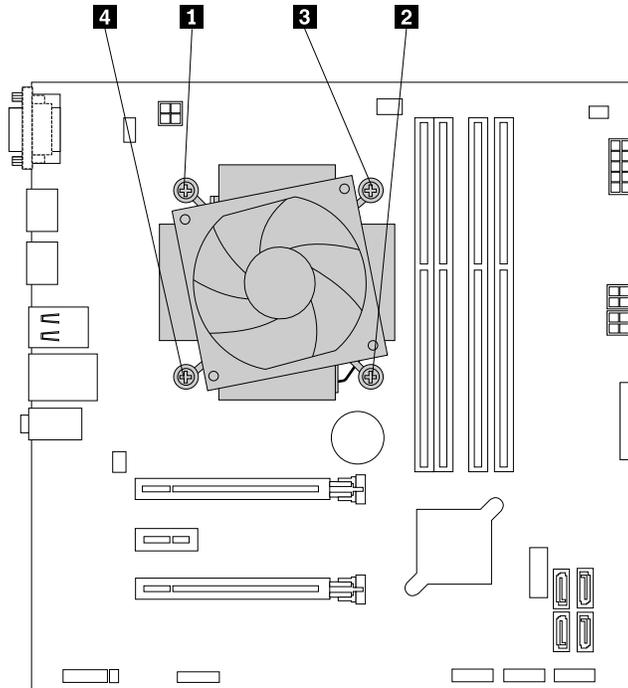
Removendo o conjunto de dissipador de calor e ventilador
